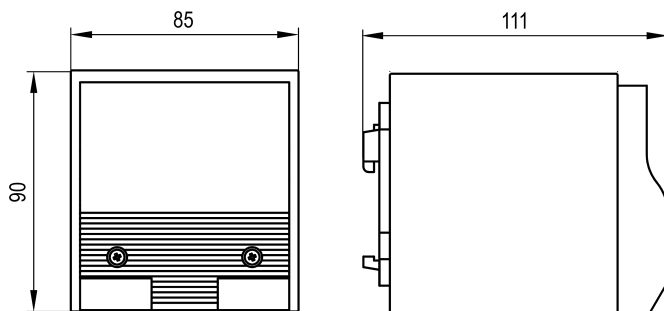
Габаритные размеры МТК-ЕFххх
